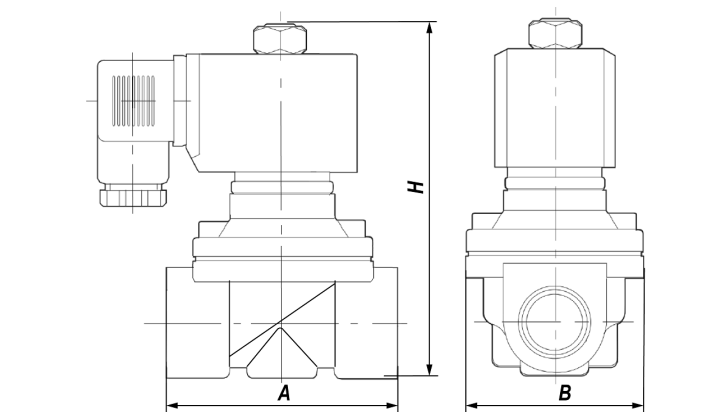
Габаритные и установочные размеры (клапаны с ДУ 16...40 мм)
